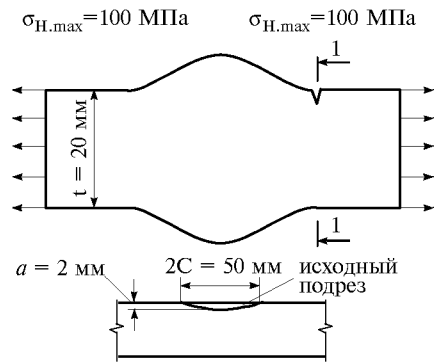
Расчетная схема стыкового сварного соединения
